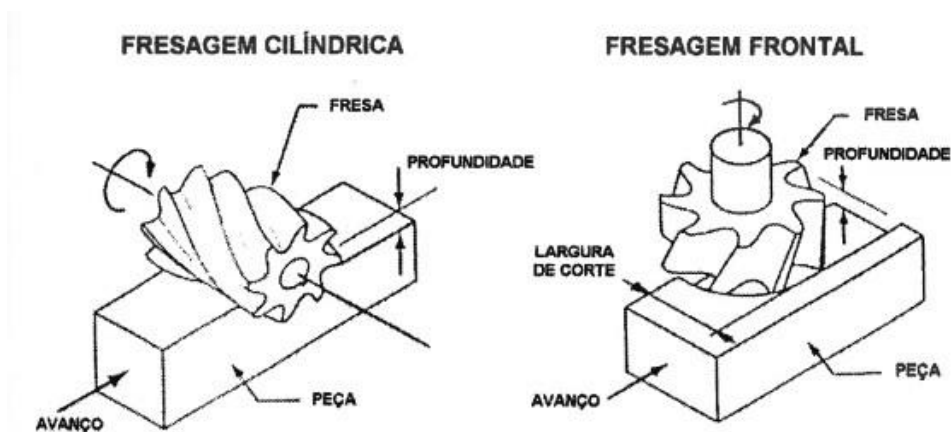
Fresagem cilíndrica e fresagem frontal [19].
